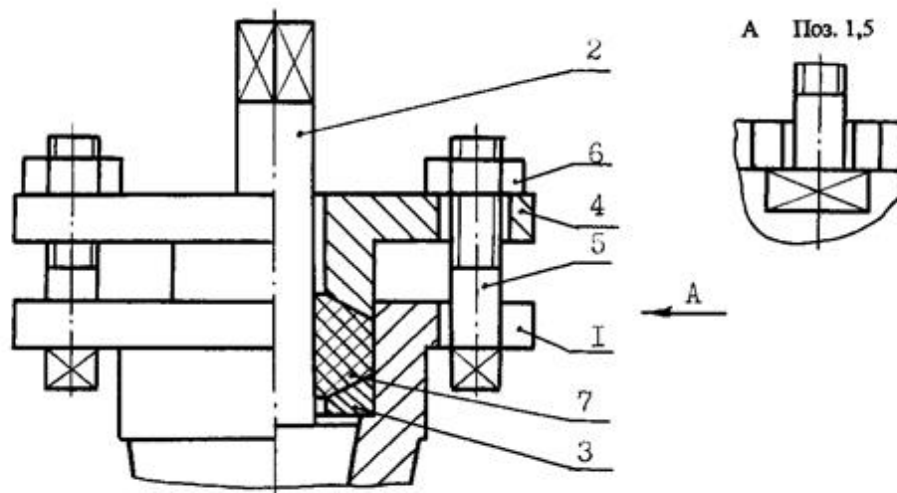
Конструкция сальникового устройства с закладными болтами
